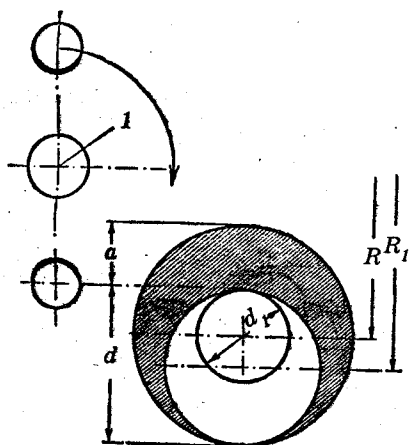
Изменение радиуса кривошипа и диаметра шейки при шлифовке коленчатого вала:
